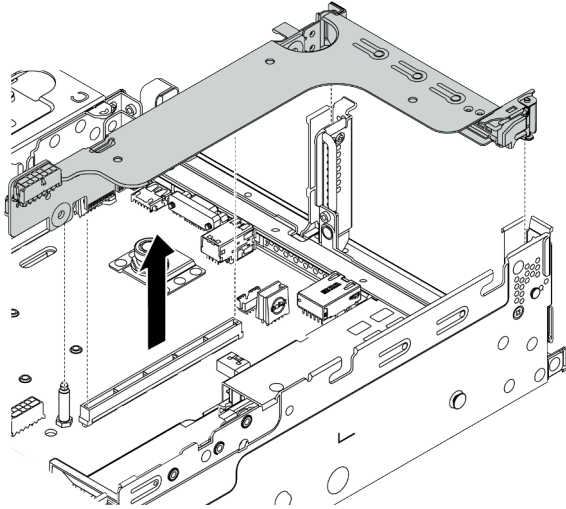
Rimozione dell'assieme verticale 1/2 (staffa verticale a uno slot)
